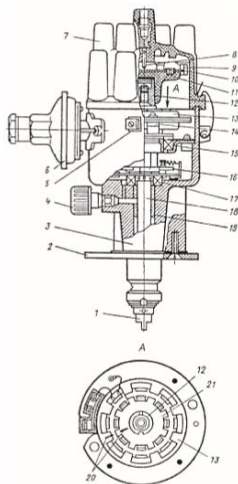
Датчик распределитель 24.3706: 1 – присоединительный шип; 2 – пластина октан -корректора; 3 – корпус; 4 – масленка; 5 – изолированный вывод; 6 – вакуумный регулятор; 7 – крышка распределителя; 8 – центральный электрод (уголек); 9 – электрод крышки распределителя; 10 – электрод ротора распределителя; 11 – ротор распределителя; 12 – втулка; 13 – статор датчика; 14 – опора; 15, 17 – подшипники; 16 – центробежный регулятор; 18 – валик; 19 – медно -графитовая втулка; 20 – риски; 21 – ротор МЭД
